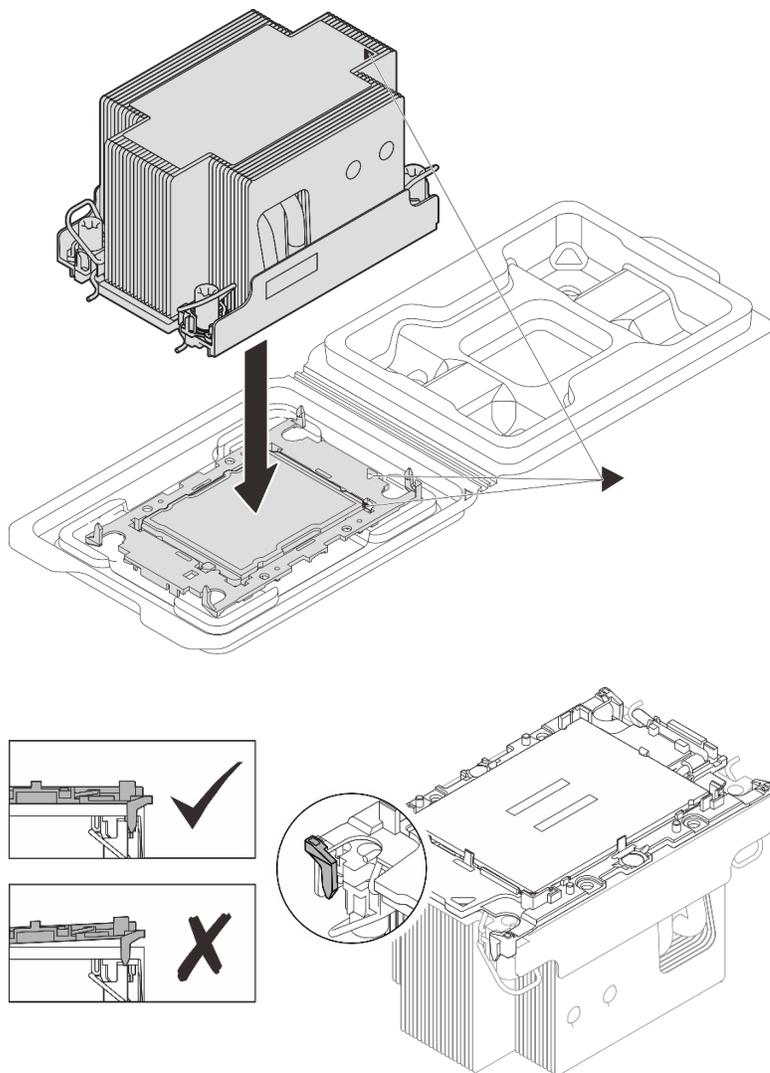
Assemblage du module de processeur-dissipateur thermique avec le processeur dans le plateau d'expédition
